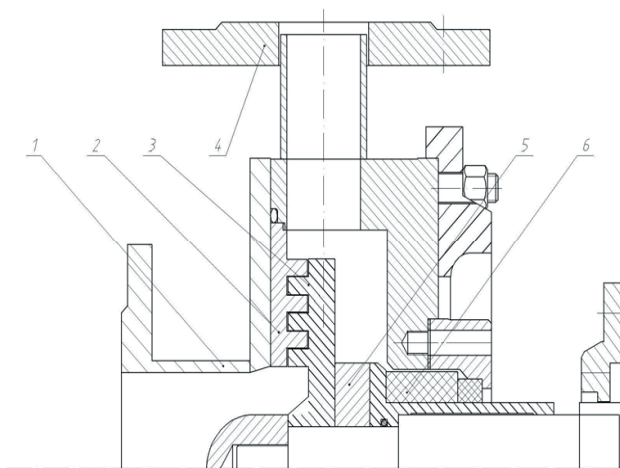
Креслення проточної частини стану для випробувань РДАГ
